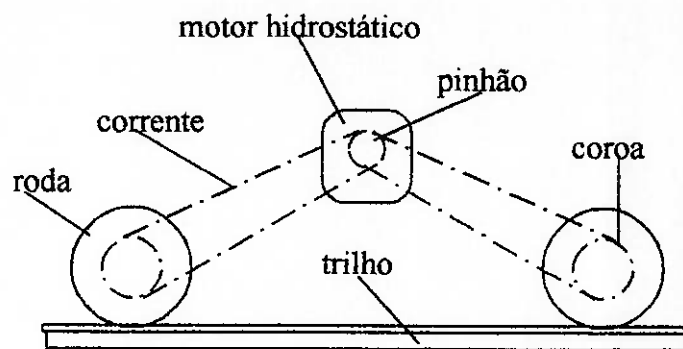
Transmissão Final por corrente e rodas dentadas.
